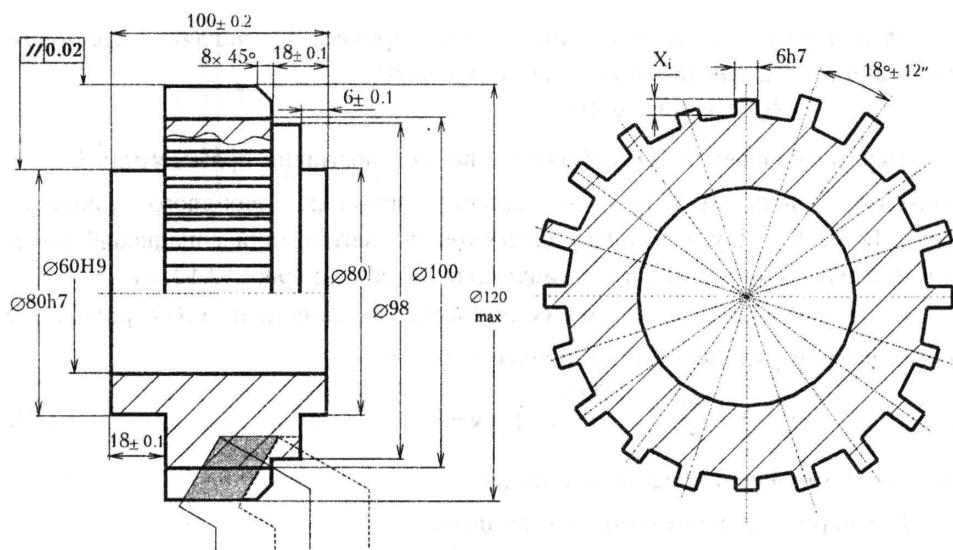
Ескіз базової заготовки з прямокутними виступами, висота яких є випадковою величиною
